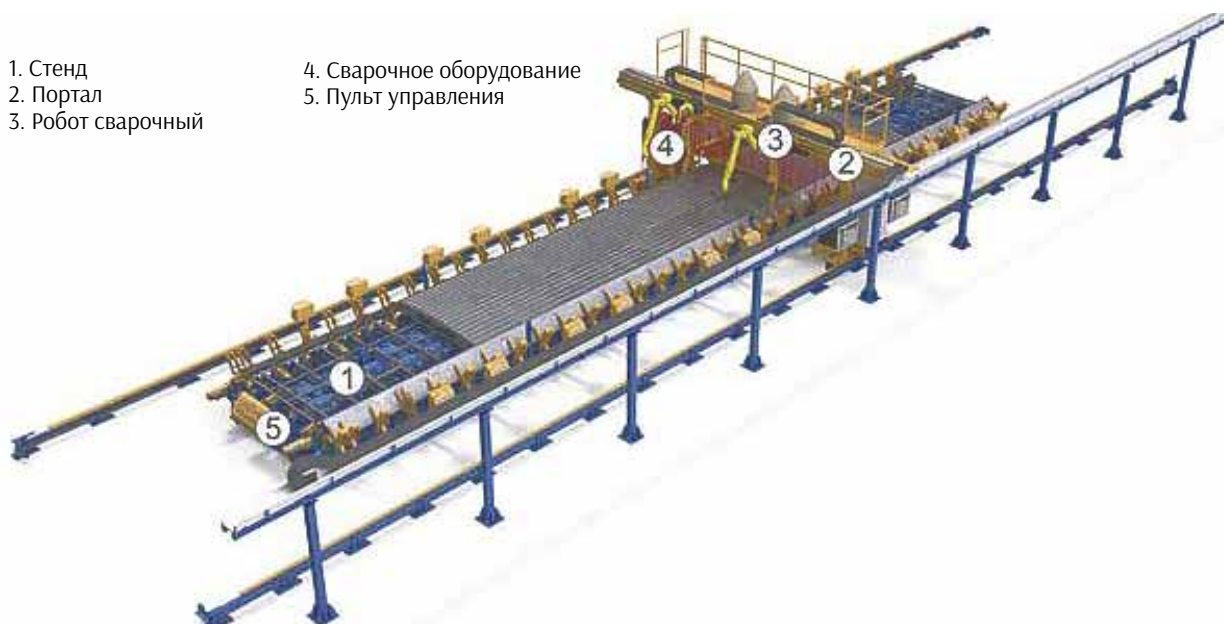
Общий вид роботизированного комплекса для сварки крыш вагонов метро:
